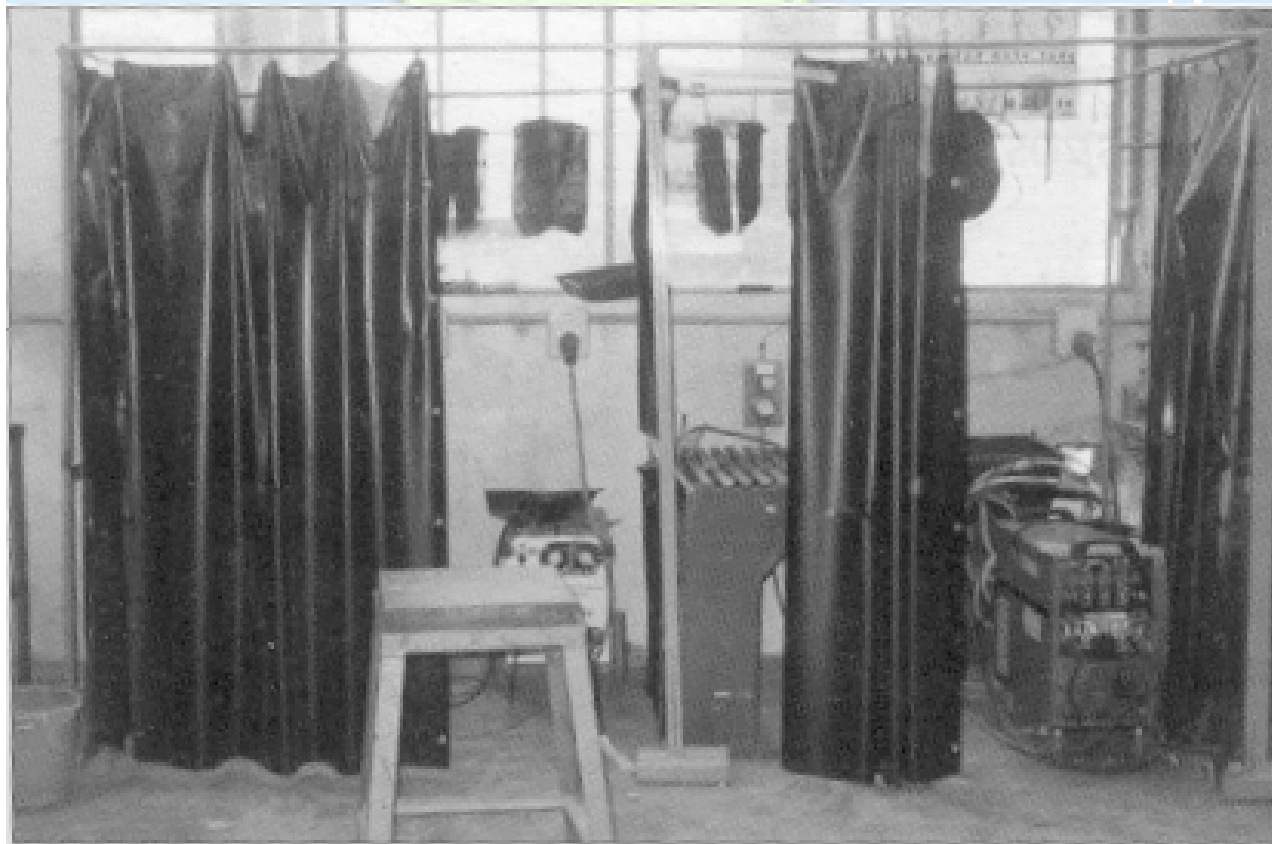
Puestos de trabajo de soldadores.
